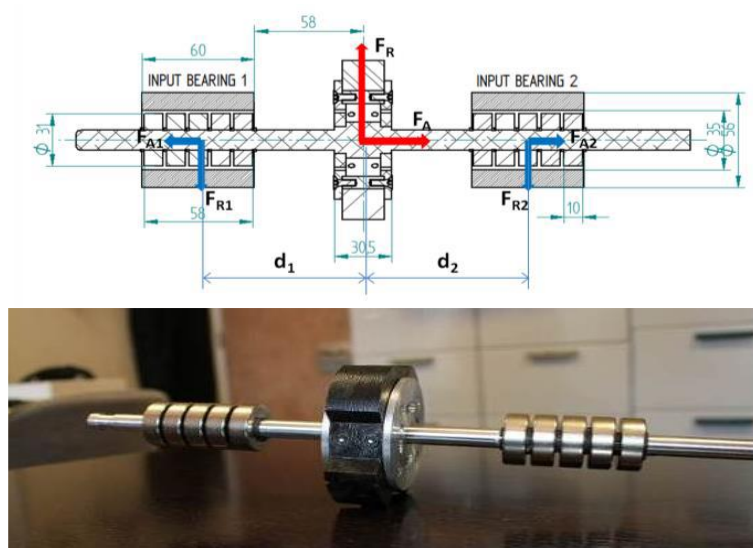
Схема и прототип механического чертежа оси, поддерживаемой сверхпроводящими магнитными подшипниками (SMB).
